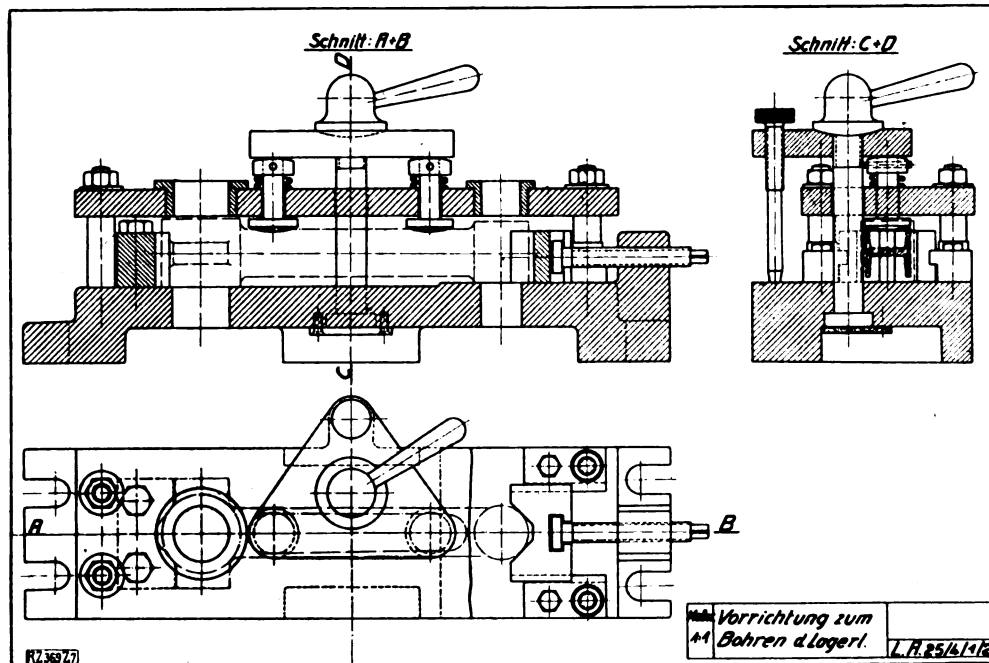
Bohrvorrichtung für Schubstange, angefertigt in den Zeichenübungen für Werkzeugmaschinen an der Maschinenbauschule Köln.
